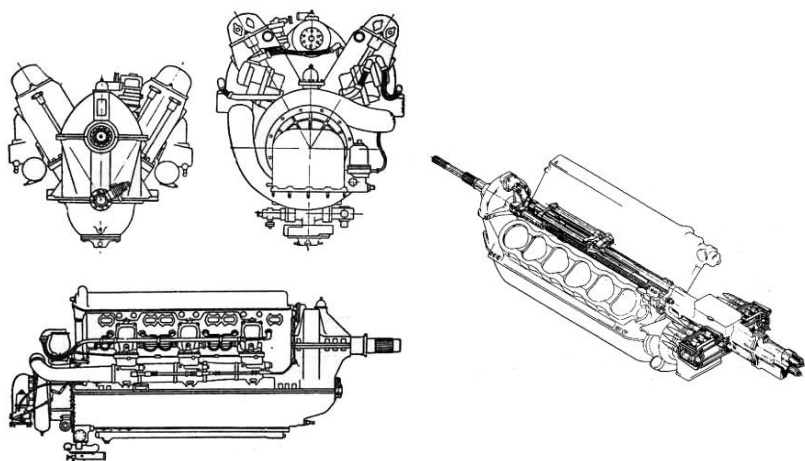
Общий вид авиадвигателя М-105 (слева) и схема установки авиапушки Ш-37 в развале блока цилиндров (справа)
